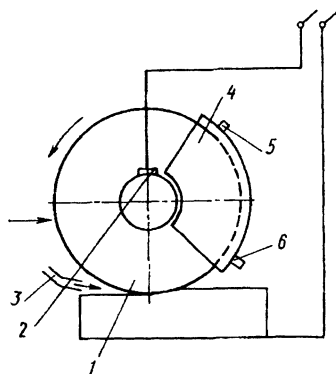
Схема рабочей головки для воздушно-дуговой резки вращающимся электродом
